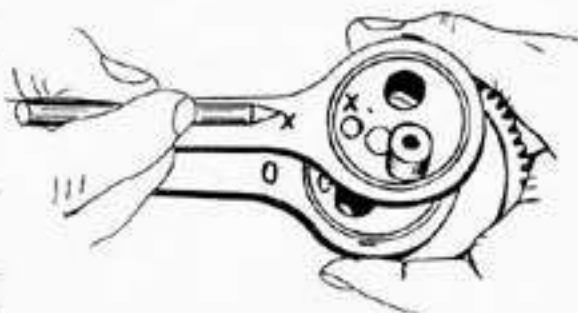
Auch die Pumpstangen-Teile müssen vor dem Ausbau gegenseitig gezeichnet werden.
